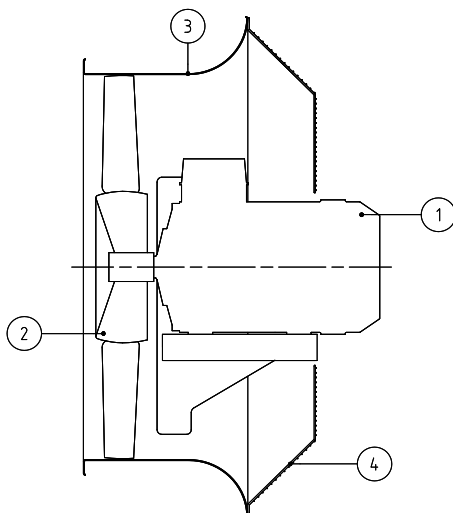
Zusammenbau des Axialventilators in Ausführung 4
